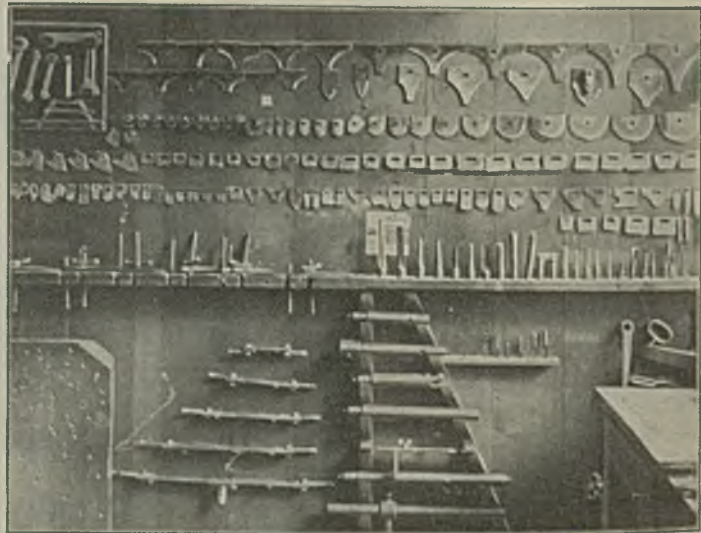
Werkzeuge der Fräsmaschine Bauart Wadkin.
